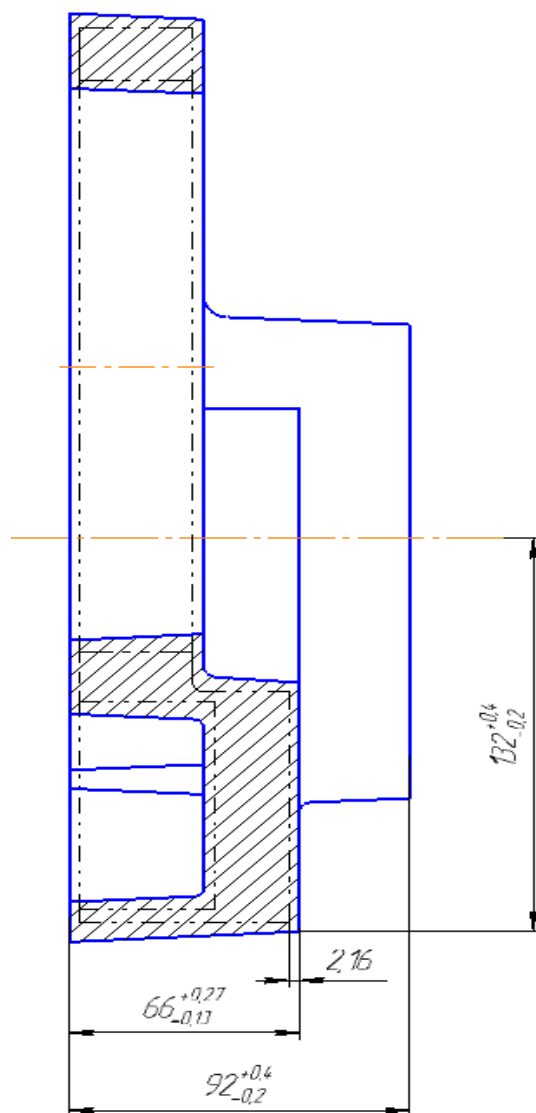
Эскиз заготовки, полученной методом литья под давлением
